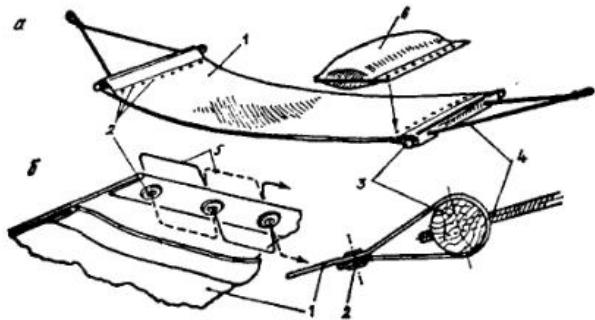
Гамак: а — общий вид; б — детализировка.
